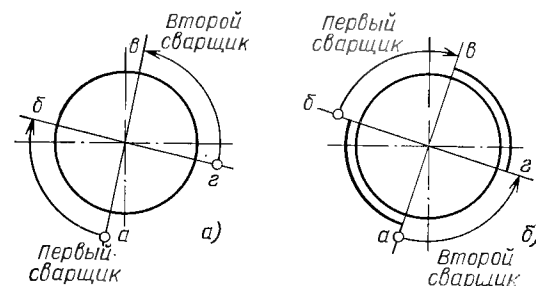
Порядок наложения валиков первого слоя шва при сварке вертикального неповоротного стыка труб диаметром 219 мм и более двумя сварщиками.
